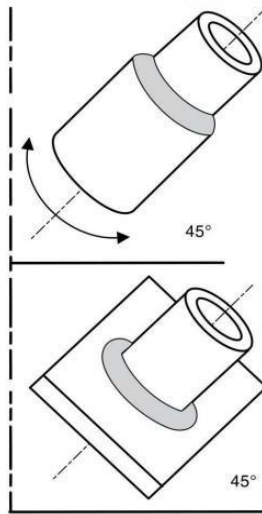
9 *Multiple Welding Test Position 6G*⁹
